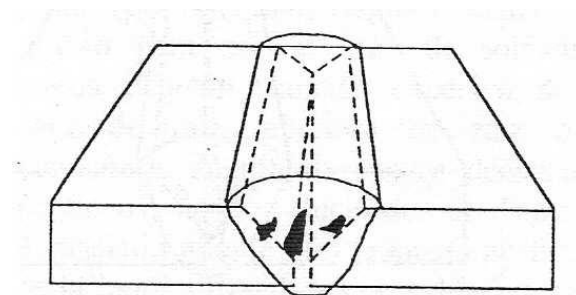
Porosidad en soldadura por arco sumergido en acero ASTM A709. [25]
